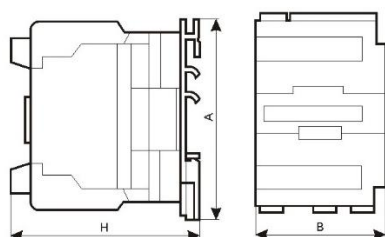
Контактор неревверсивный ПМЛ-5160М
